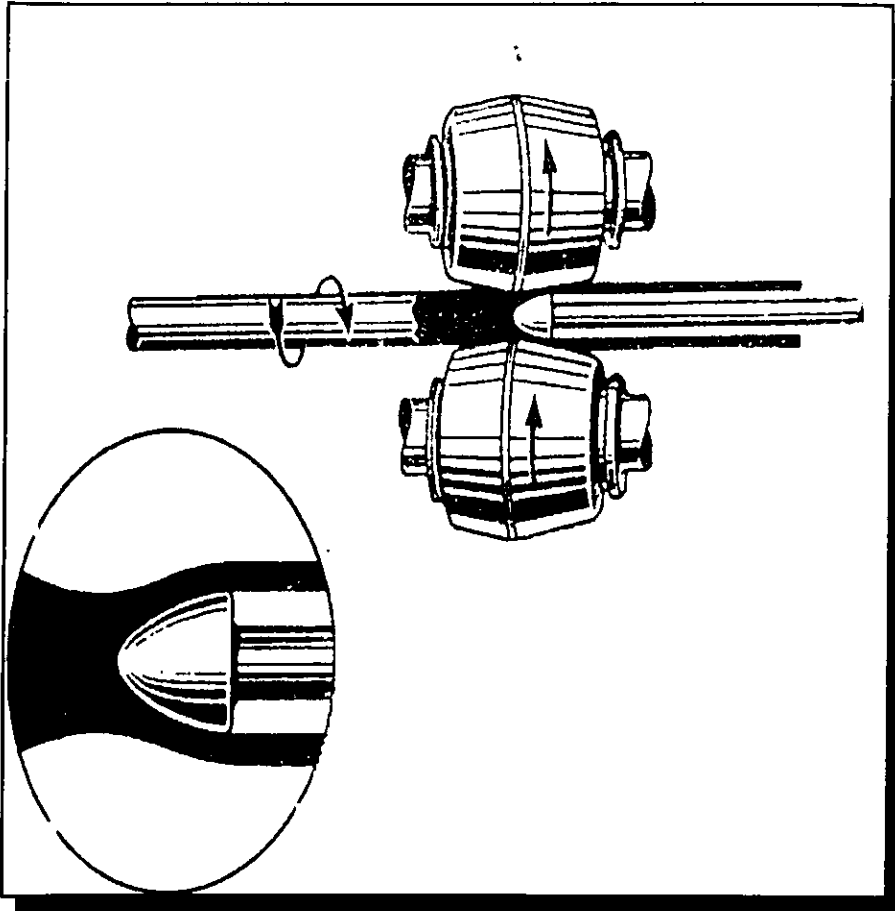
Mandril cilíndrico para fabricación de tubo sin costura
